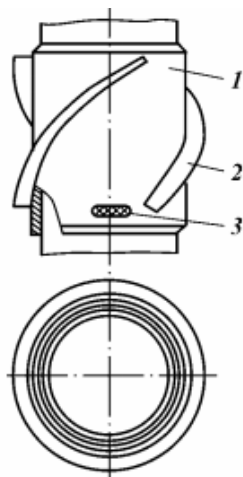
Турбулизатор типа ЦТ: 1- корпус неразъемный; 2-лопасть;3- клин спиральный
